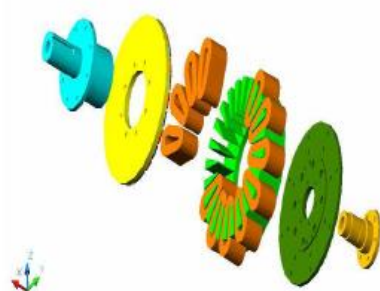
Machine à flux axial 1 stator/1 rotor avec bobinage sur dents [16]
